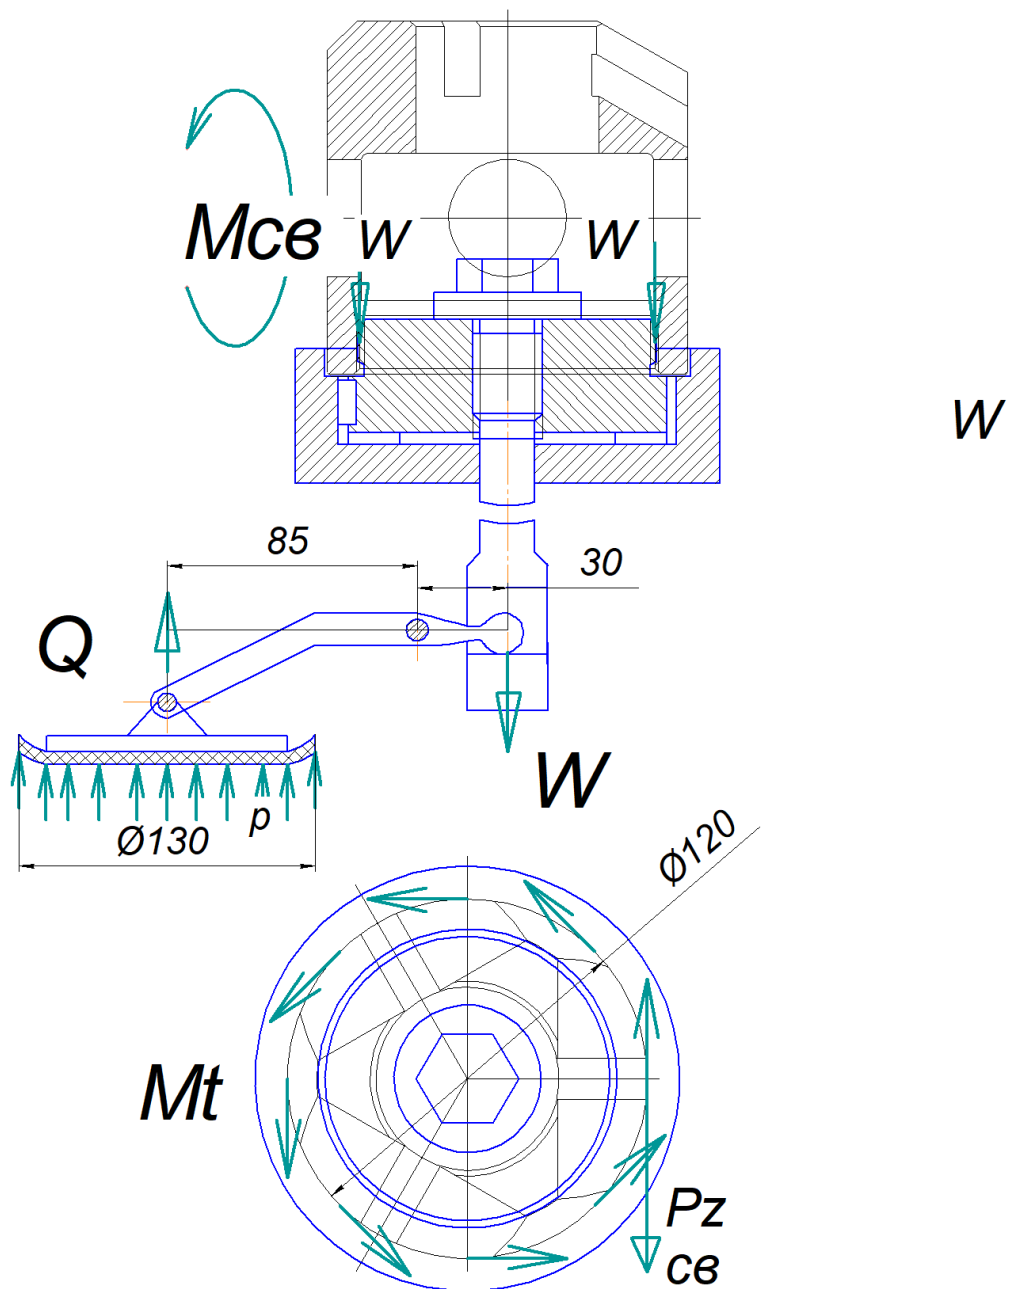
Розрахункова схема пристрою для п'ятикоординатного верстата
